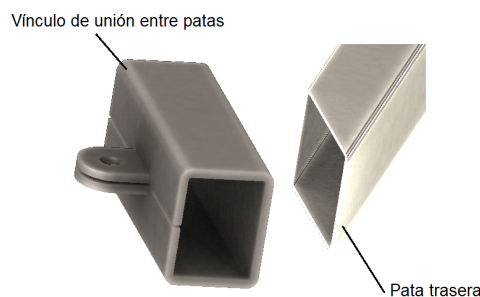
Soldadura del Vínculo de Unión entre pata trasera y delantera.
